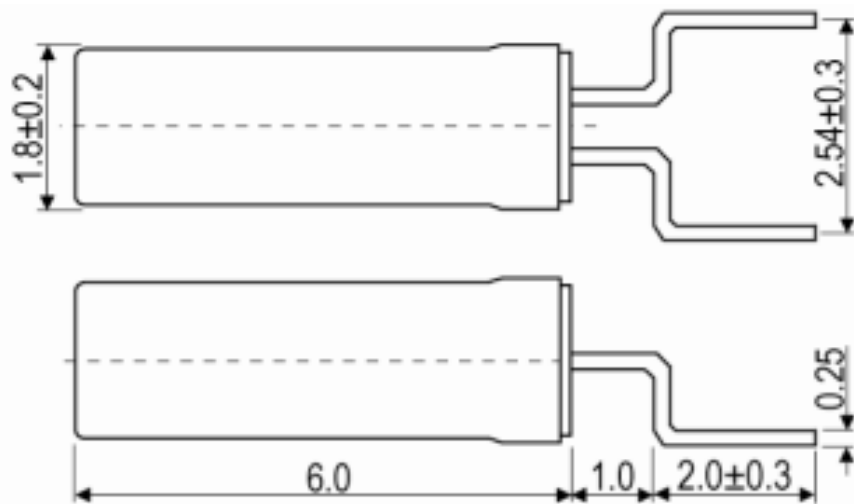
Габаритні розміри 32.768KCFPX-56R
